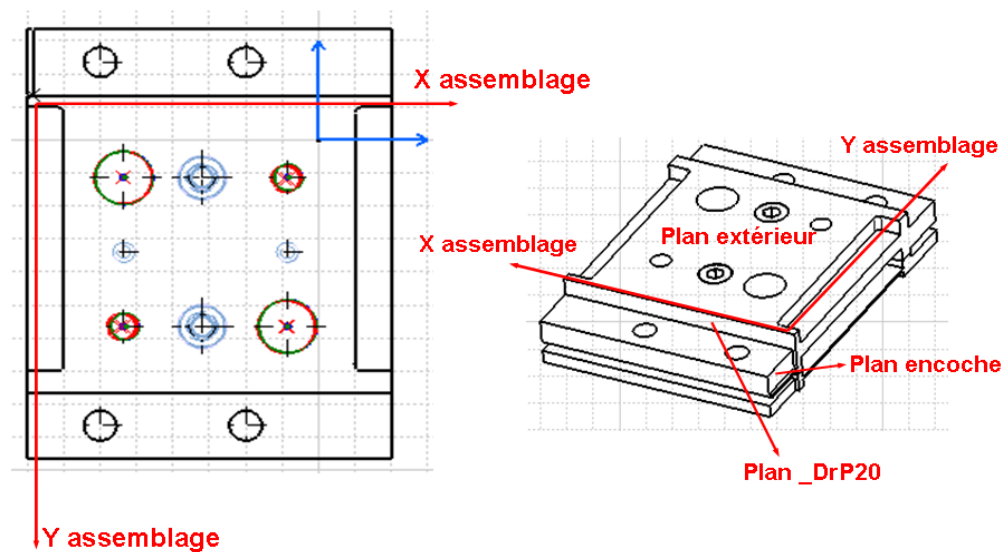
Repère de mesure de la pièce assemblée (repère d'assemblage)
